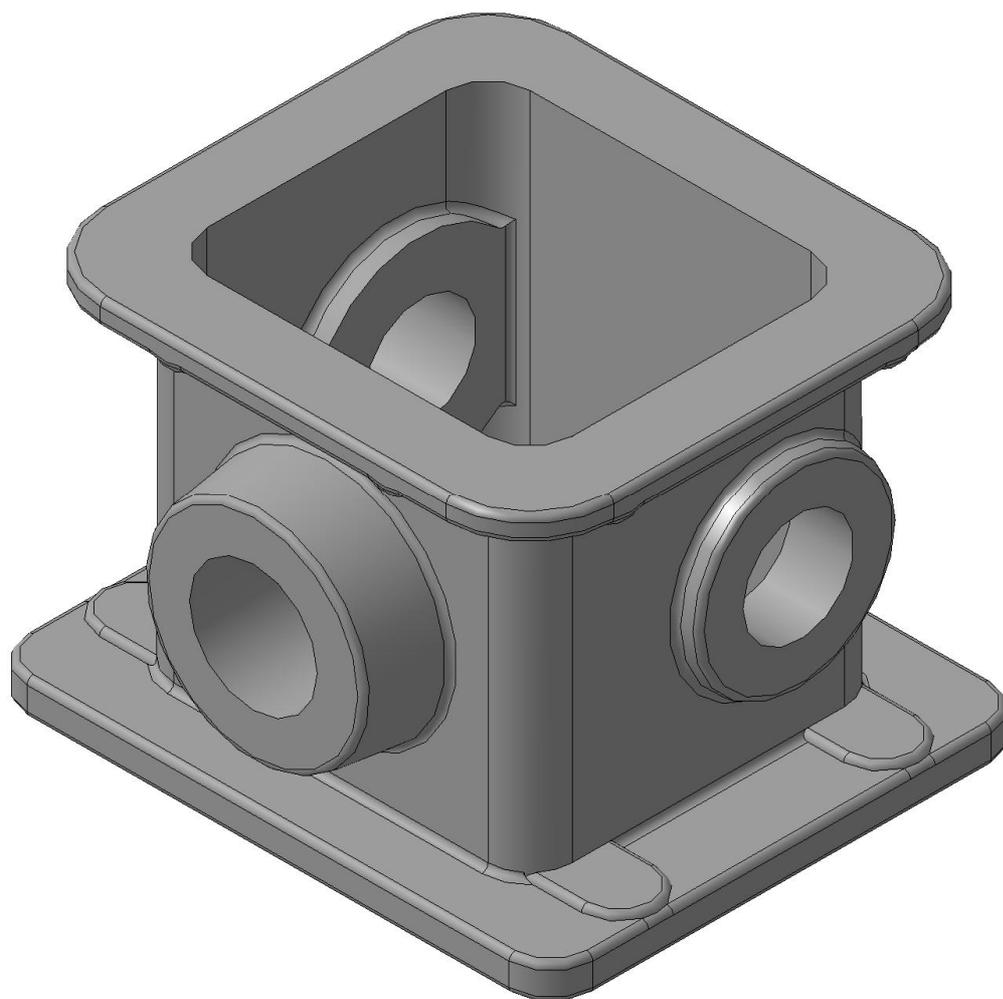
3D-модель заготовки детали «Корпус червячного редуктора»
